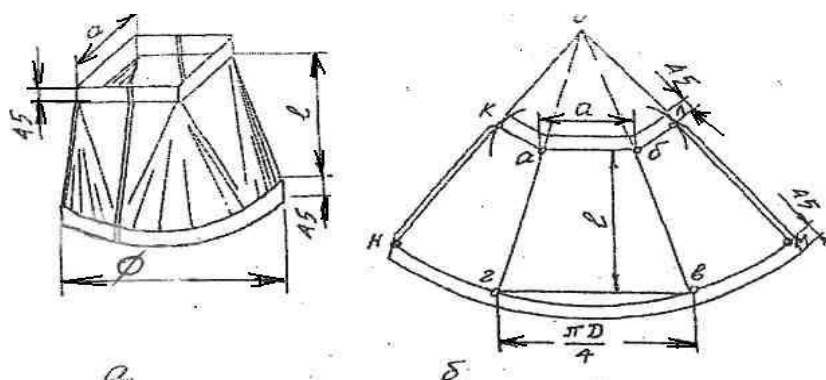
Побудова розгортки переходу з круглого перерізу на квадратний:
